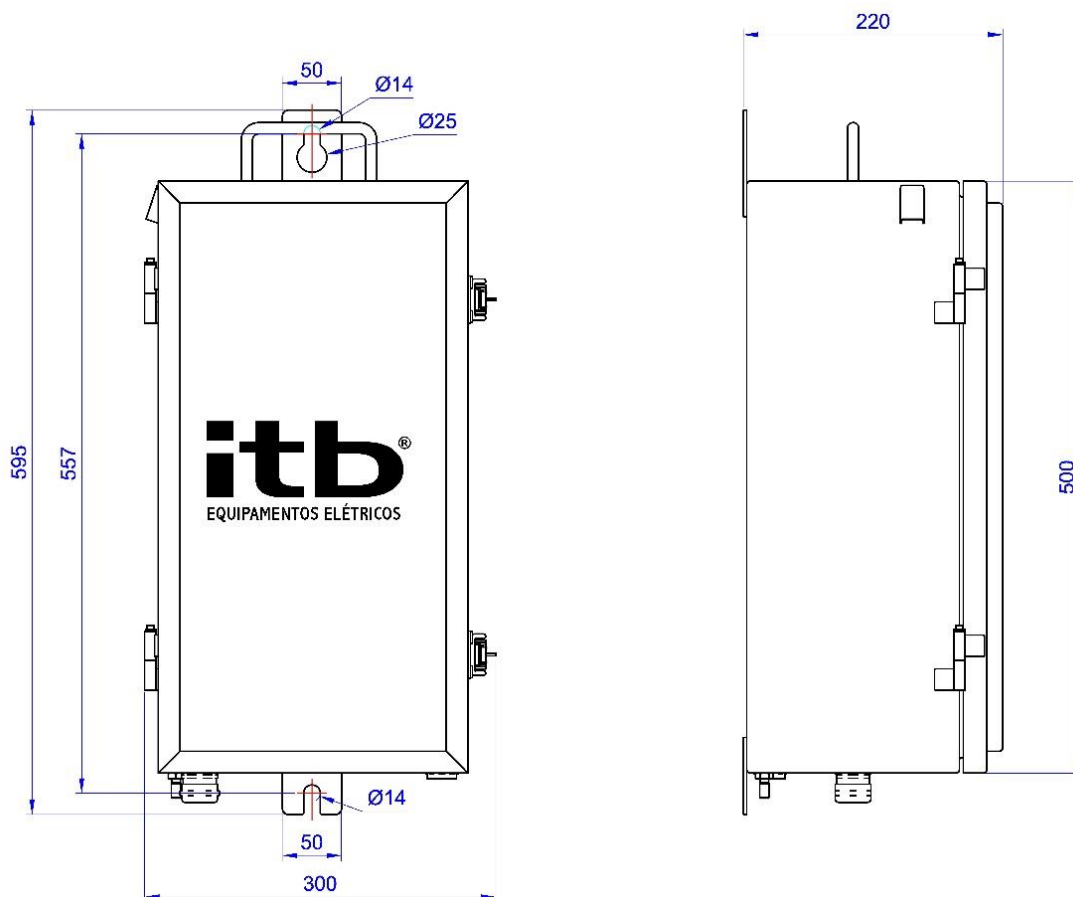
Dimensional externo da caixa de controle (medidas em mm).
